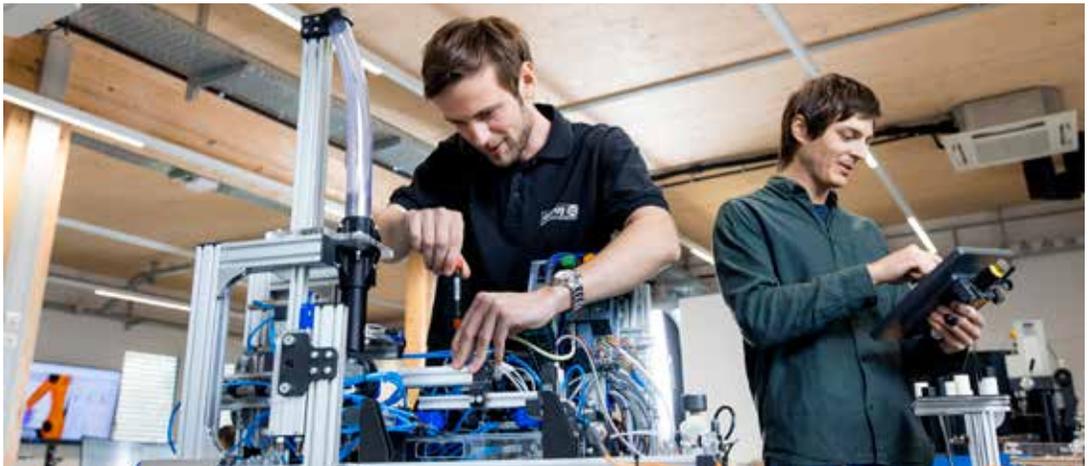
Prototyp-Aufbau einer Richtmaschine für Drahtelemente
